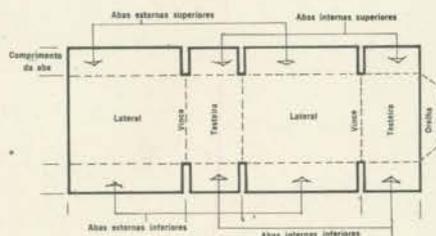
Elementos de uma caixa normal desarmada de papelão ondulado.
